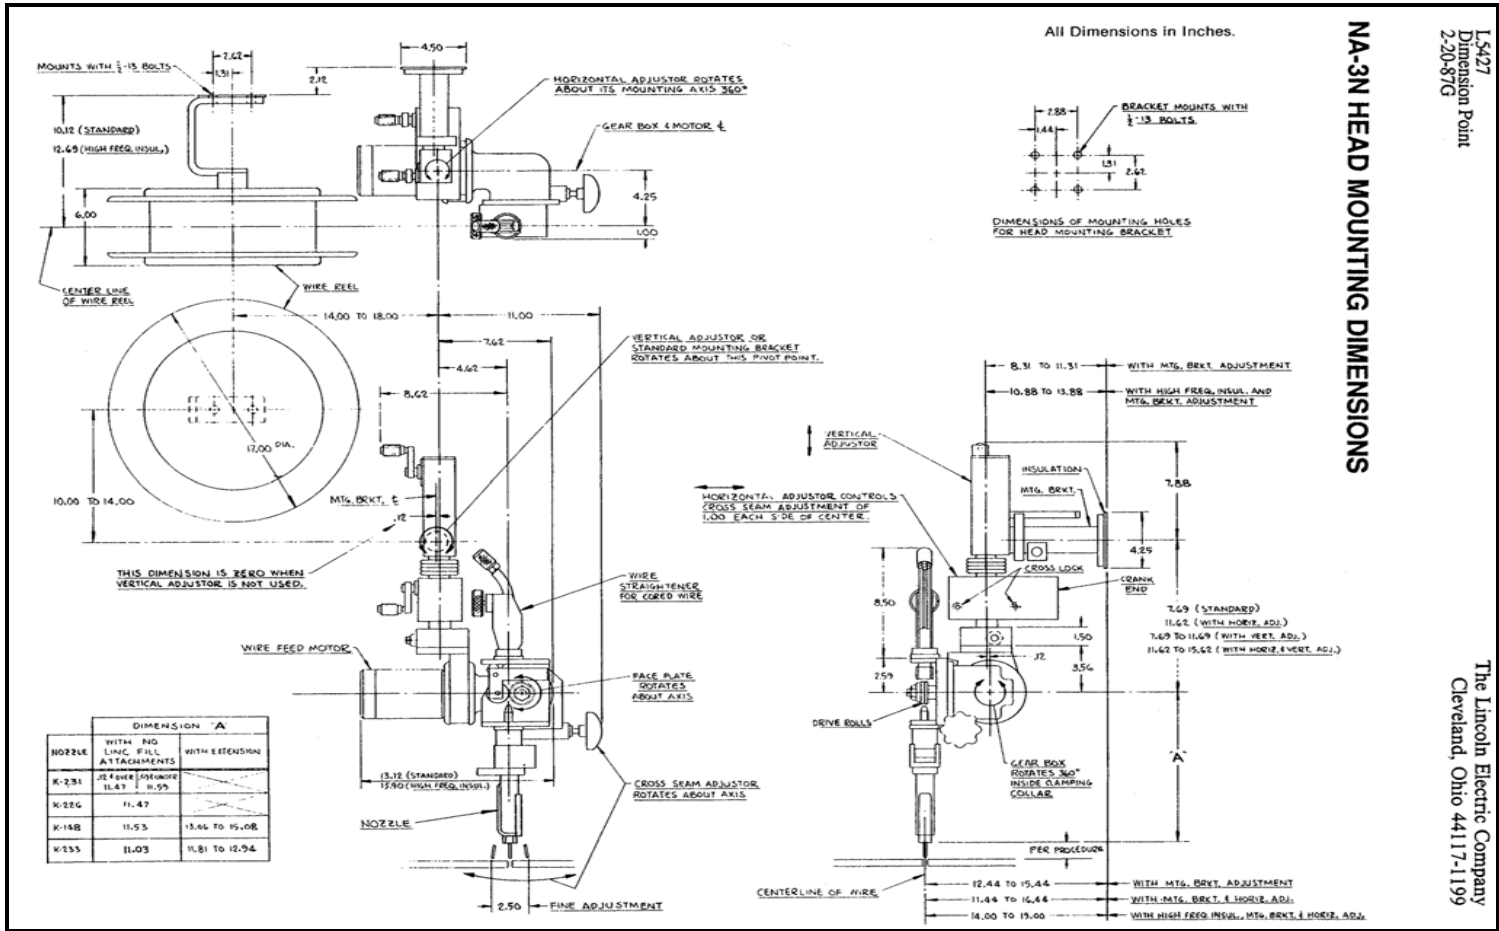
Dimensiones del cabezal de soldadura que utiliza la maquina formadora para la soldadura de las tuberías helicoidales
